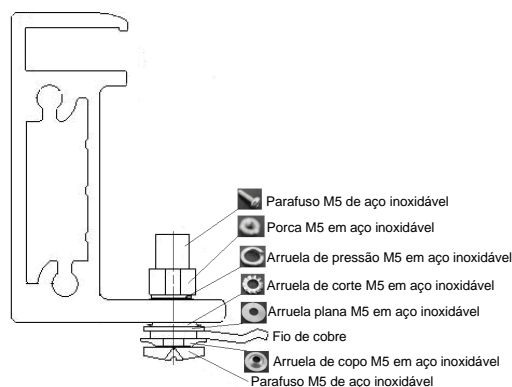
Aterramento da moldura de alumínio com fio de cobre
